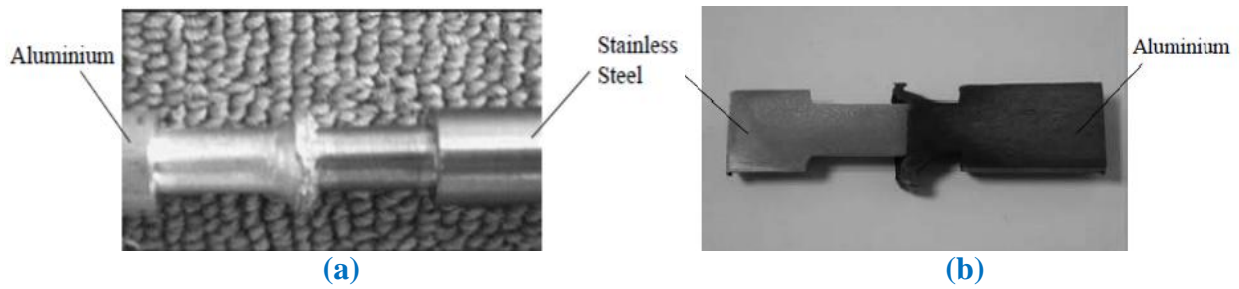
Joint AISI 304/Aluminium soudé par friction rotative : a) Photo du joint, b) Photo de l'interface du joint [14].
